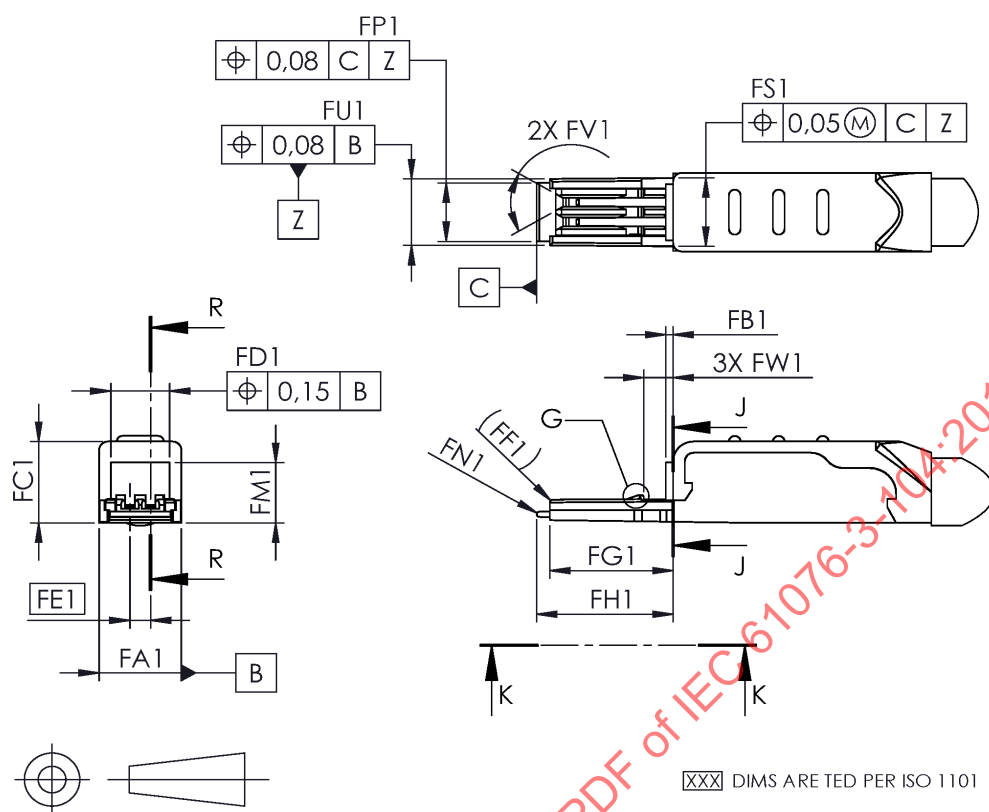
Dessin 2 de la variante 04Tableau 8 – Dimensions du dessin 2 de la variante 04*Dimensions en millimètres
